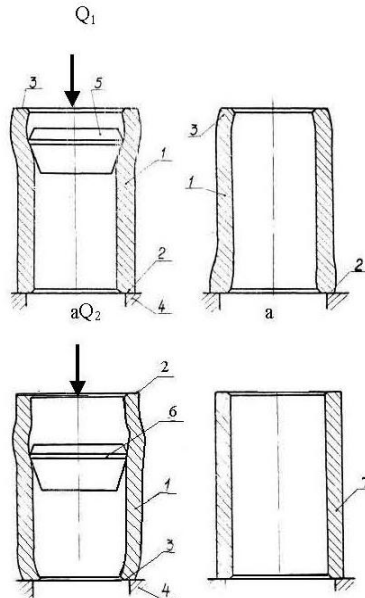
Схема раздачи поршневого пальца в парное число проходов с изменением опорного торца
